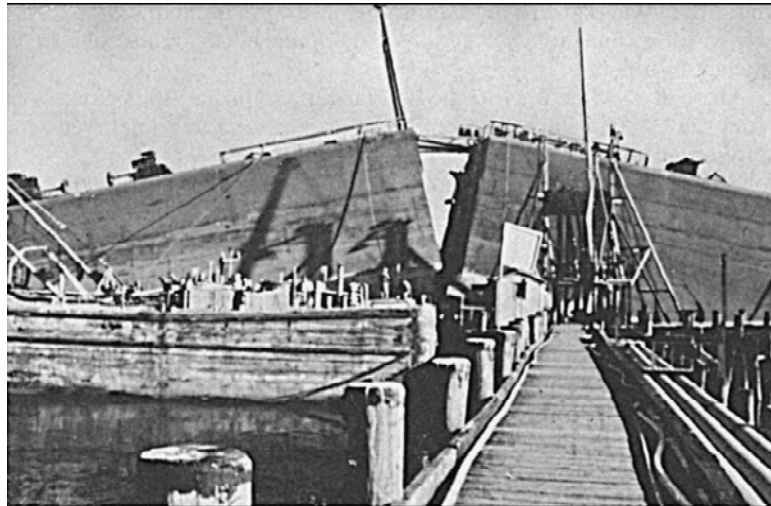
Fractura del buque I.O.S. 3301 ocurrida en 1972.
